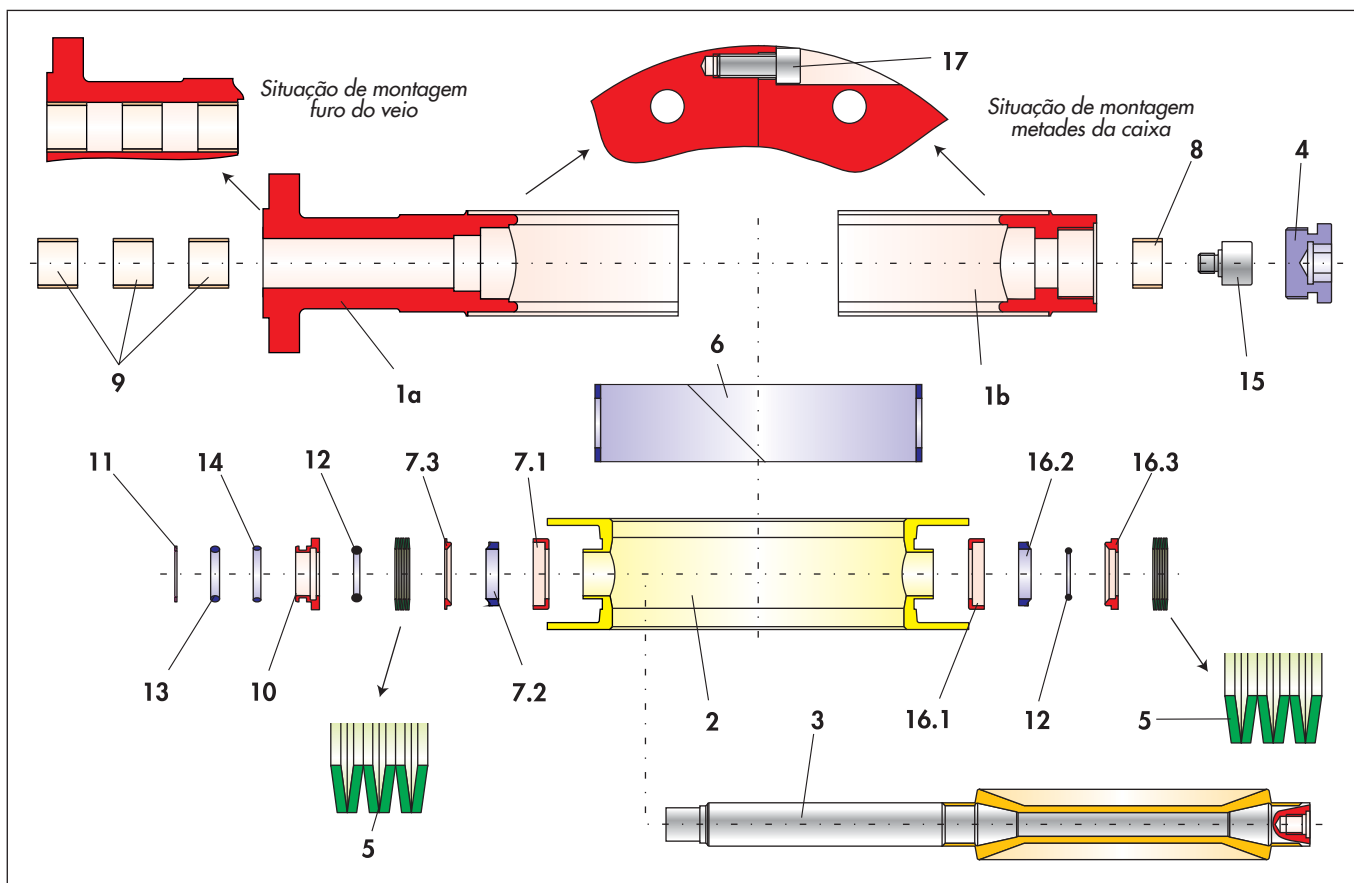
Desenho explodido da válvula borboleta BR 10e
